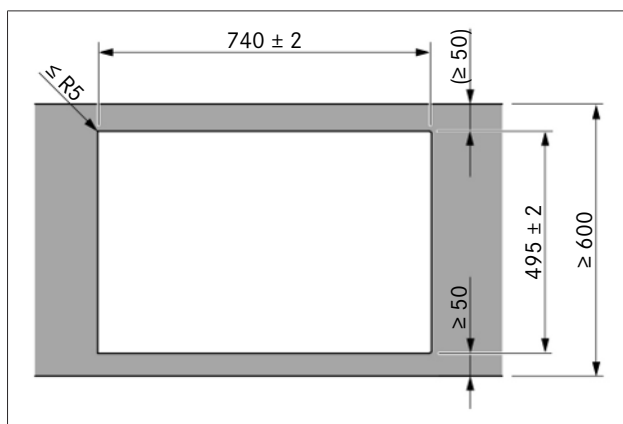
Dimensioni intaglio per montaggio in battuta
